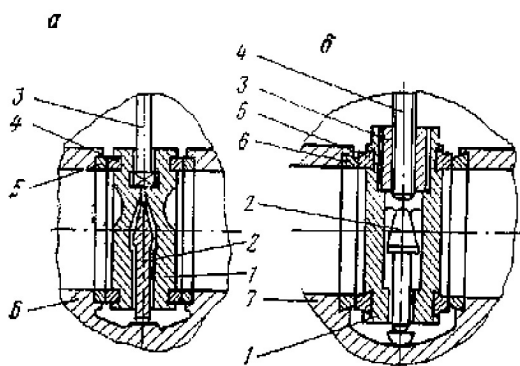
Затвор двухдисковых параллельных задвижек: а) с выдвижным шпинделем: 1 — диск; 2 — грибок; 3 — шпиндель; 4 — уплотнительное кольцо; 5 — седло; б) с невыдвижным шпинделем: 1 — диск; 2 — грибок; 3 — ходовая гайка; 4 — шпиндель; 5 — уплотнительное кольцо; 6 — седло; 7 — корпус
